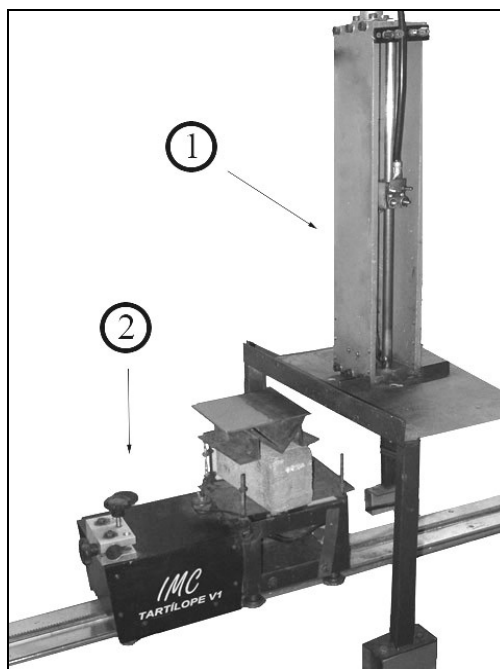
Vista de bancada para soldagem semi-automática do Laboratório de Soldagem da UFSC: 1) sistema para deslocamento automático do eletrodo; 2) controle da velocidade de soldagem.
